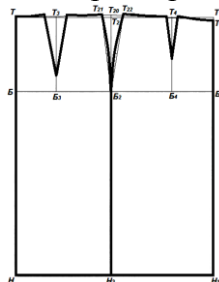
Чертеж конструкции прямой двухшовной юбки, размер 164-96-104
